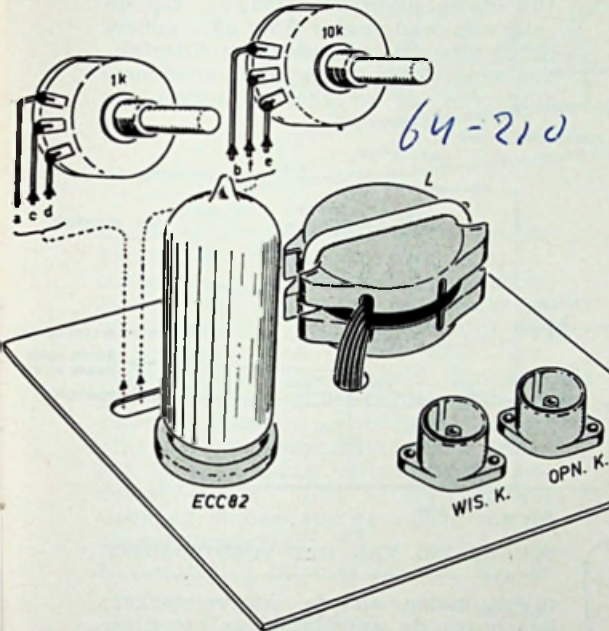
MONTAGEVOORBEELD (B in fig. 9) VOOR DE h.f. GENERATOR
